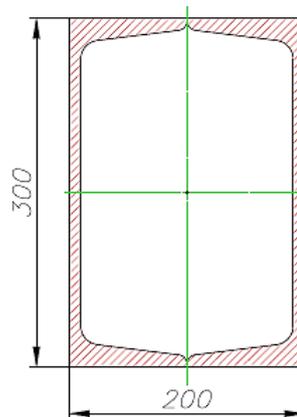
Sección transversal viga testera Fuente: (Autor)
